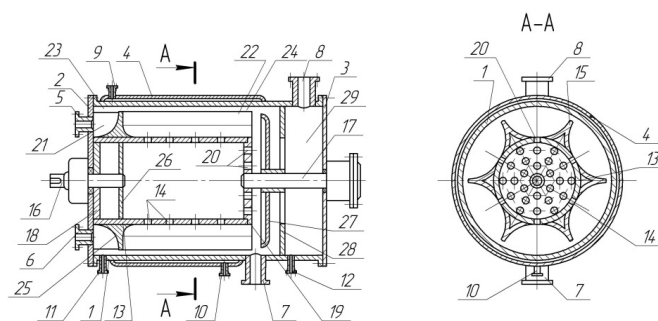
Цилиндрический ротационно-пленочный аппарат: 1 – цилиндрический корпус; 2, 3 – крышки; 4 – греющая рубашка; 5, 6 – патрубки для ввода исходного продукта; 7 – патрубок для вывода готового продукта; 8 – патрубок для присоединения к вакуумной системе; 9, 10 – патрубки для подвода пара и отвода конденсата из греющей рубашки; 11, 12 – патрубки для слива остаточной фосфолипидной эмульсии и остаточного парожирового конденсата от аппарата; 13 – перфорированный ротор; 14, 20 – отверстия; 15 – лопасти; 16, 17 – валы; 18 – диск; 19 – диск перфорированный; 21, 22 – винтообразный и прямолинейный участки лопасти ротора; 23, 24 – зазоры; 25, 26 – перегородки; 27 – сепарационный отбойник тарельчатого типа; 28 – неподвижное сепарационное кольцо; 29 – сепарационная камера
